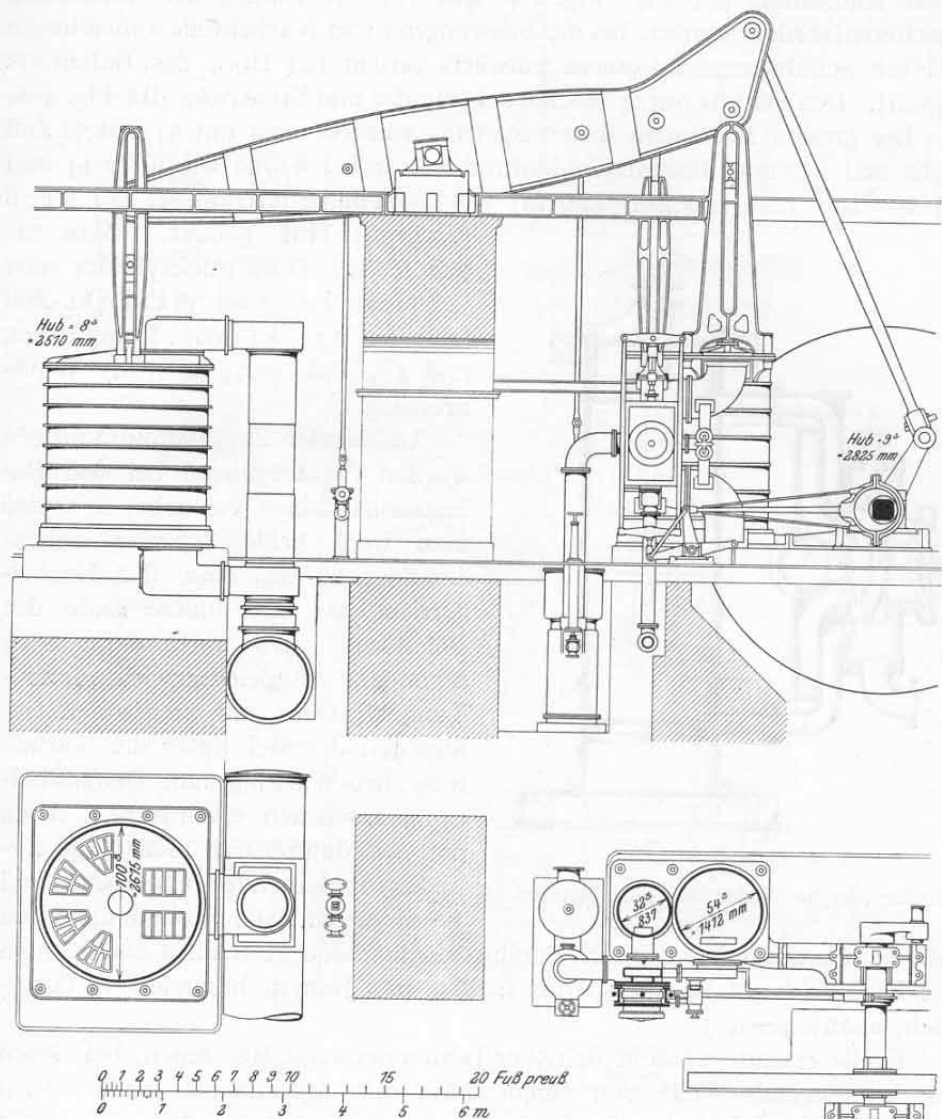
und 407. Gebläsemaschine um 1860. Märkische Maschinenfabrik in Wetter a. d. Ruhr.
